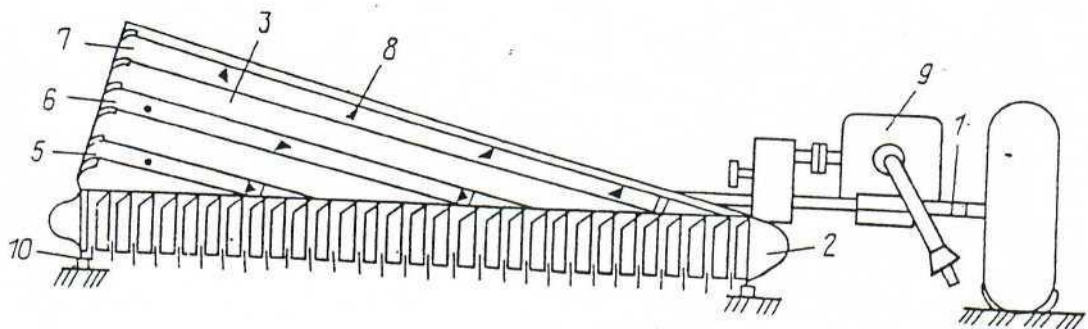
Пристрій для обертання валків [17], вид спереду
